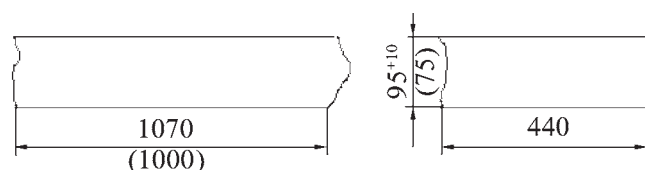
Поковка для стенки кристаллизатора: числа в скобках – габаритные чистовые размеры детали
